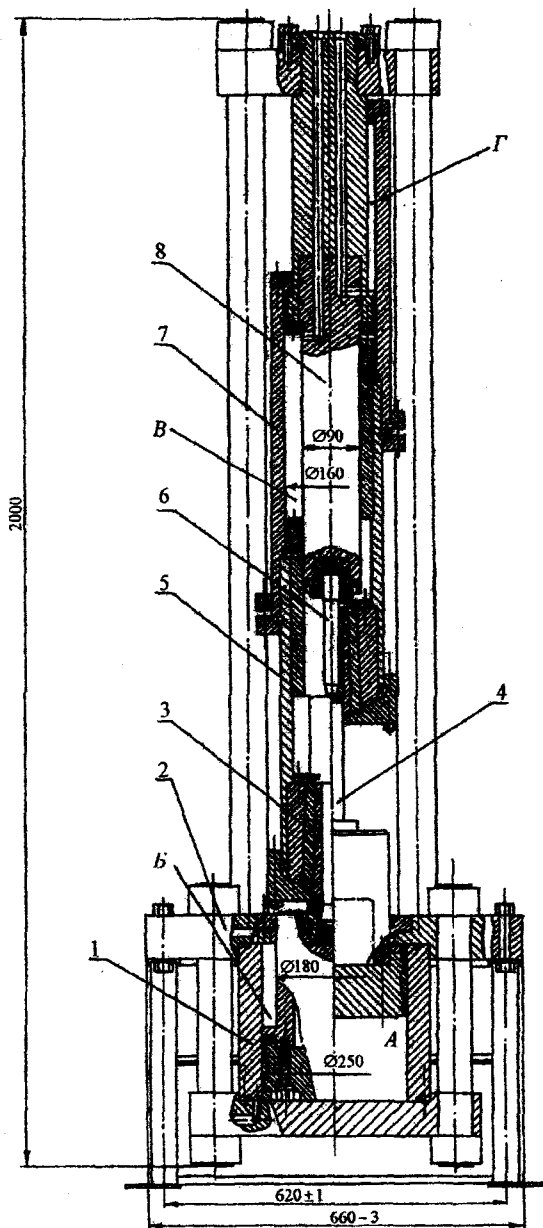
Конструкция прессы для выдавливания с активными силами трения
